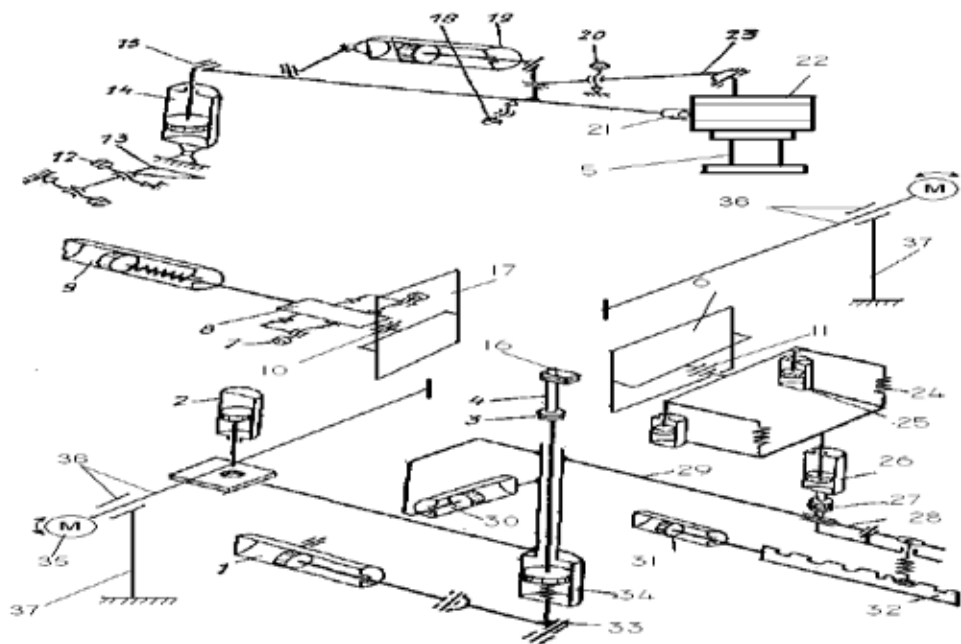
Конструктивна схема машини для шнурової затяжки заготовки з фрикційною обтяжкою МФШЗ-1
